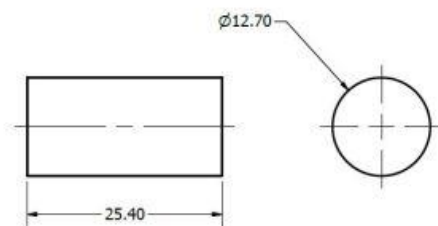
Geometría y dimensiones de la probeta para ensayo de compresión. Fuente: [10].
